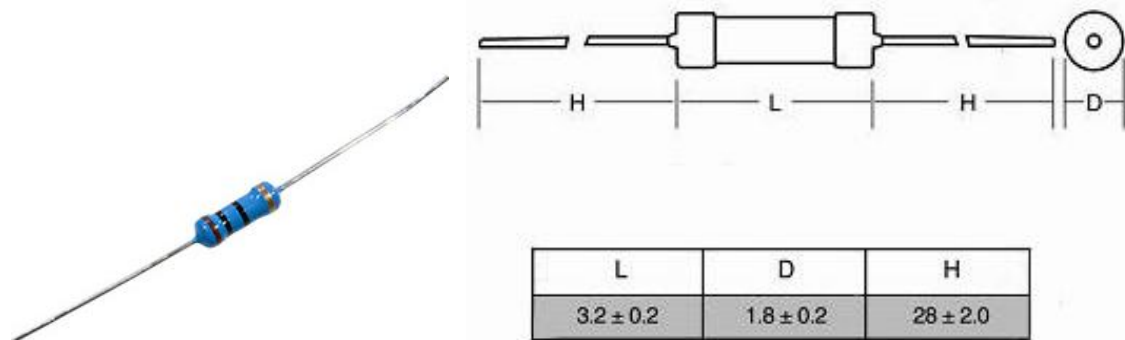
Зовнішній вигляд металоплівкового резистора MFR-0.125 з аксіальними виводами.
